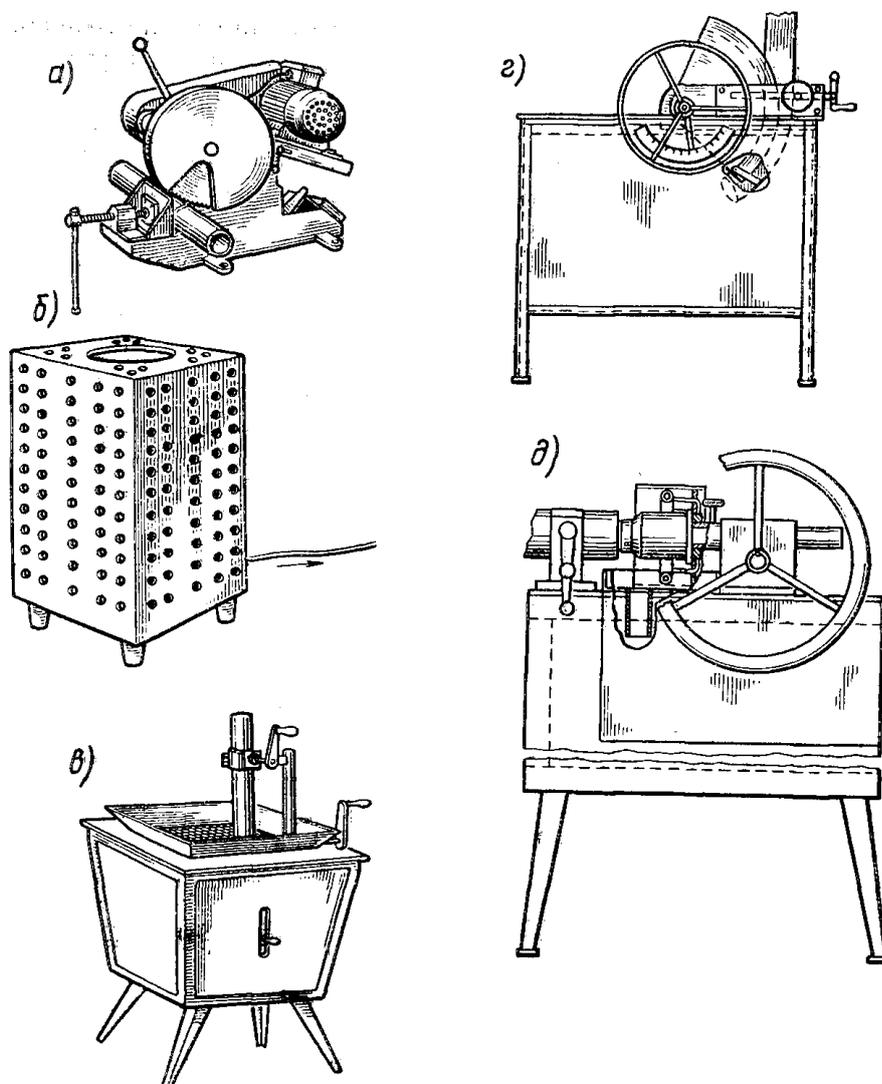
Устройство для обработки пластмассовых труб: *а* - для резки труб; *б* - для разогрева труб; *в* - для разогрева концов труб; *г* - для изгибания; *д* - для выпрессовки раструбов
